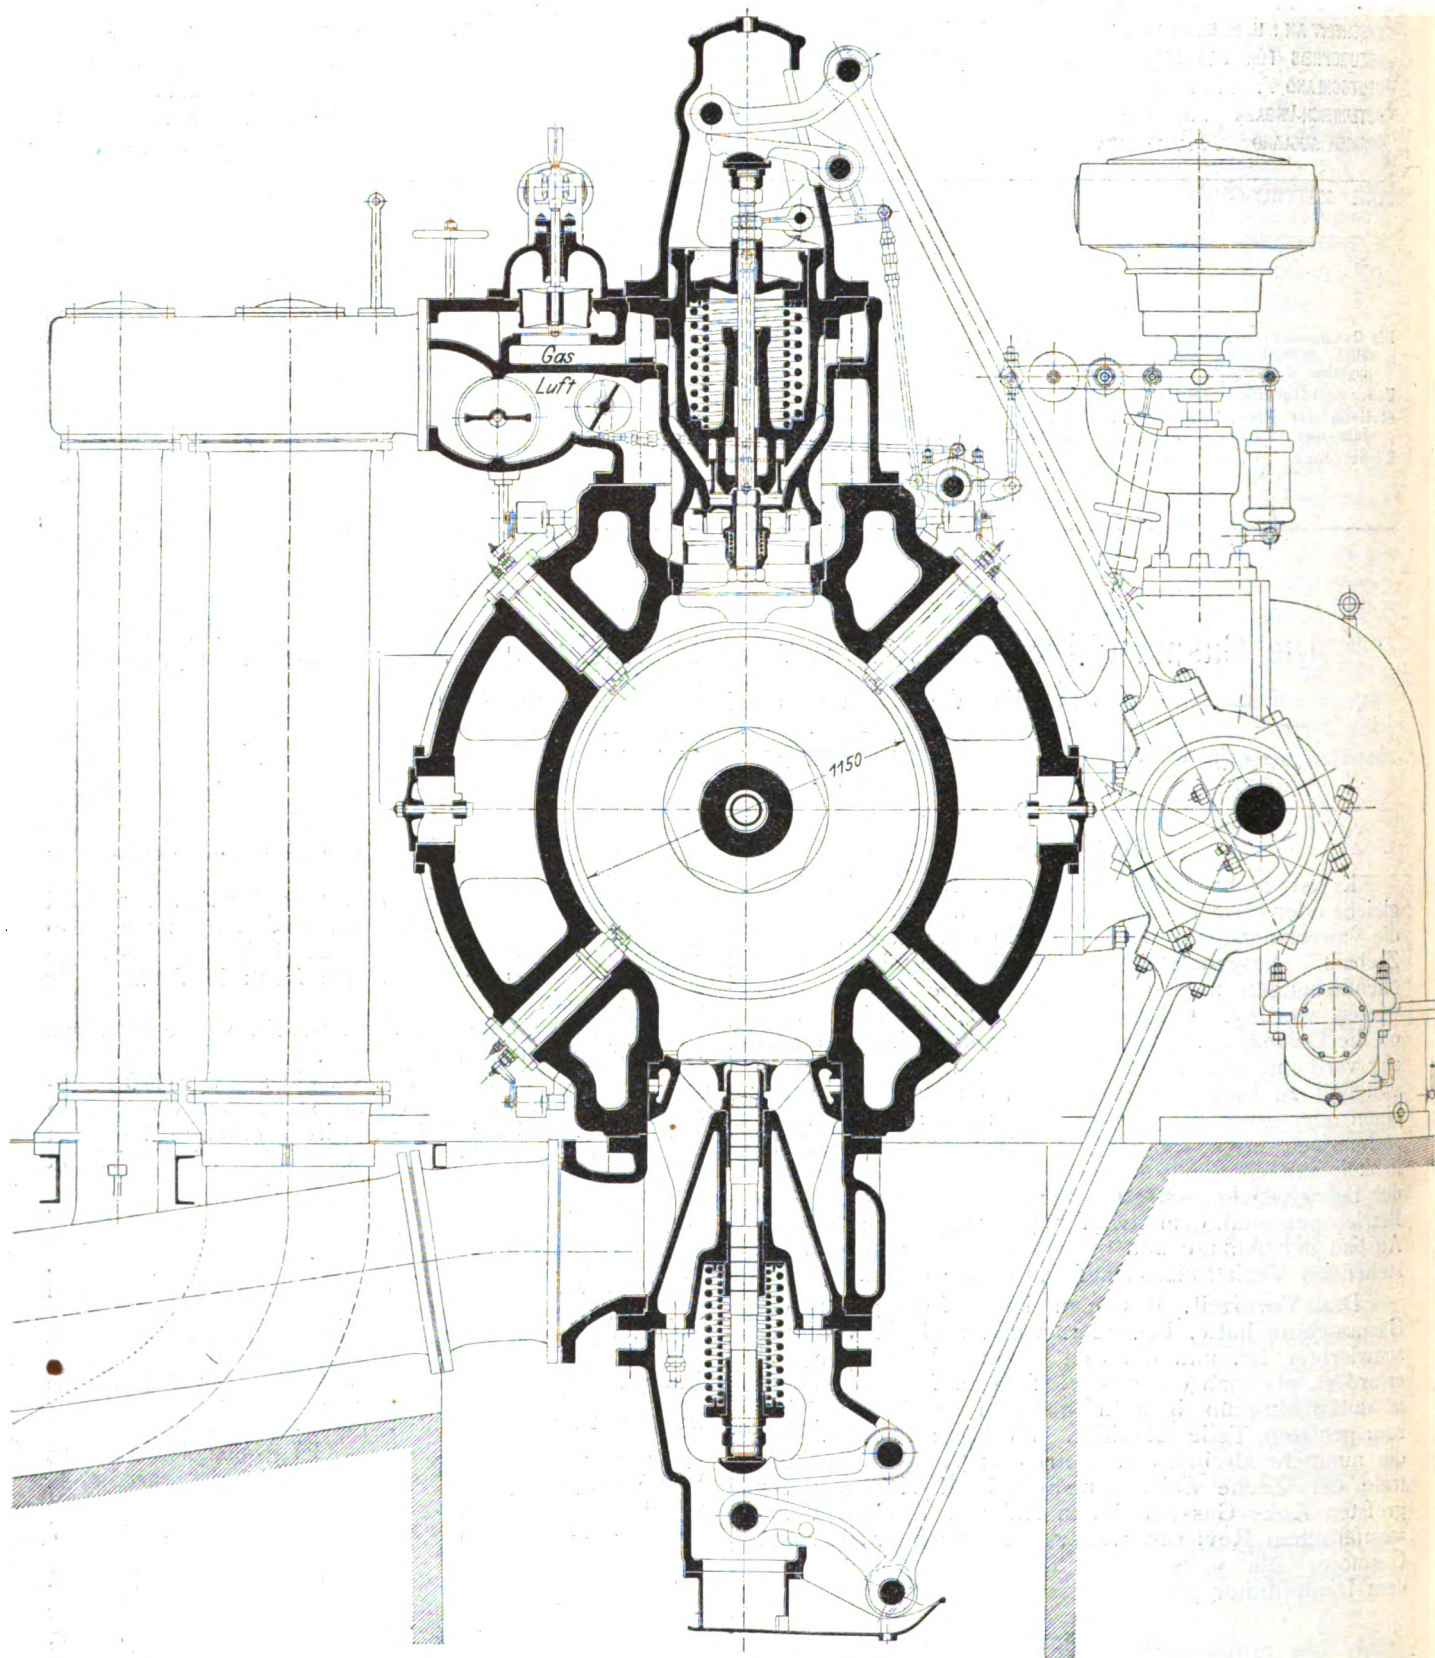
Schnitt durch den Gasmaschinenzylinder.
